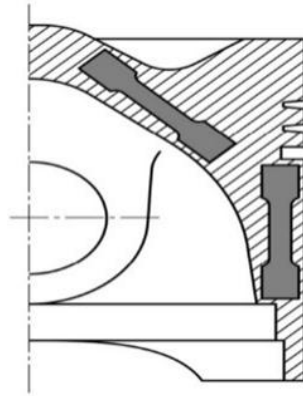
Эскиз поршня с отмеченными местами для вырезки образцов [18]
